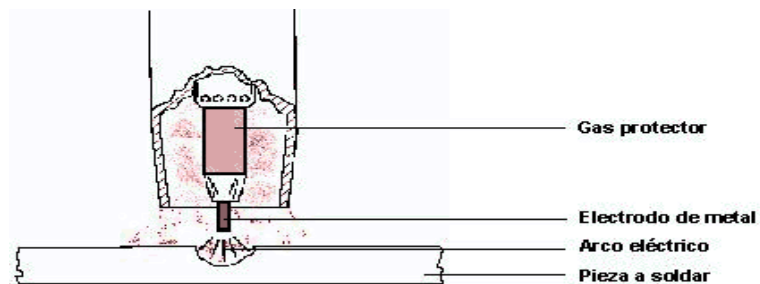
ESQUEMA DEL PROCESO DE SOLDADURA MIG
